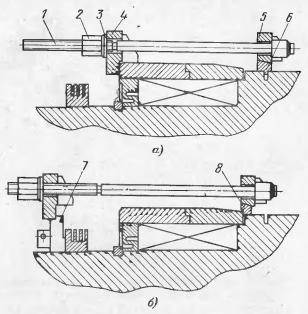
Приспособление для снятия и надевания двухпосадочных бандажей
